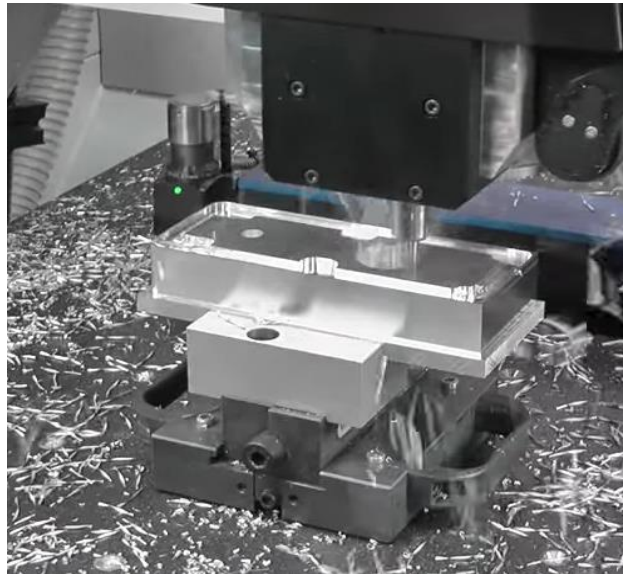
Schraubstock für prismatische Werkstück^[19]
